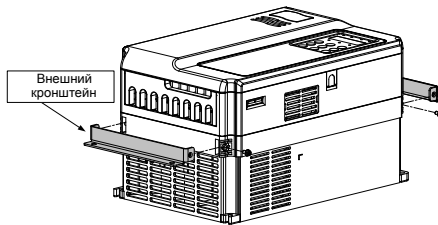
Сквозной монтаж ME320LN (пластиковый корпус)
